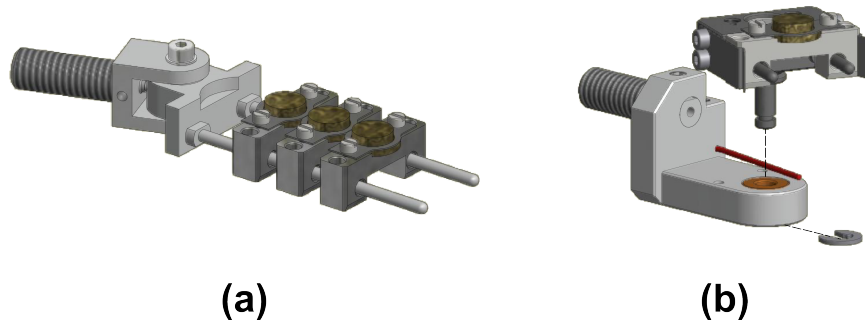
Transferstangenaufsätze: (a) Aufsatz für die Schleuse, (b) Explosionszeichnung des Aufsatzes für den Transfer zwischen den Kammern.
